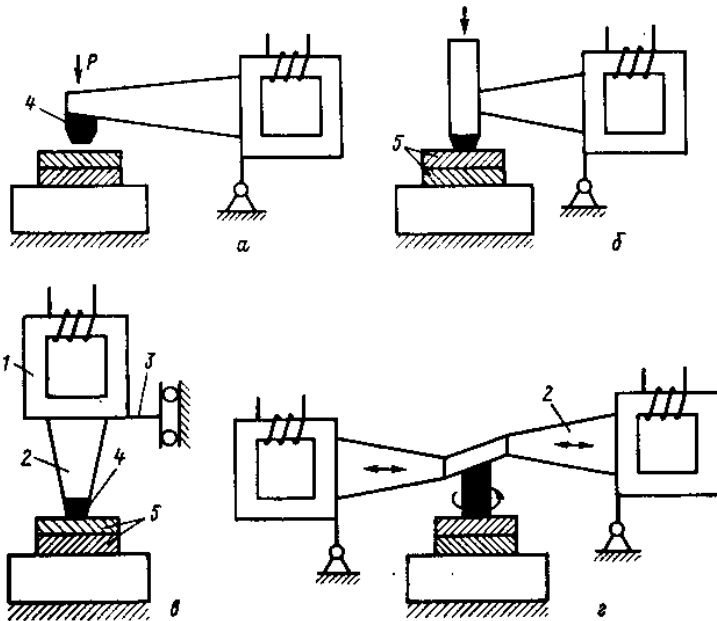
Схема типовых колебательных систем для ультразвуковой сварки металлов:
